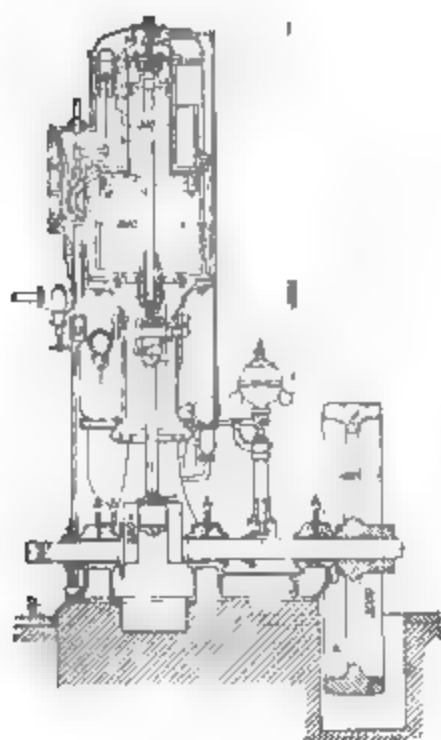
1762. Maschine zum Schmidtmotor.
